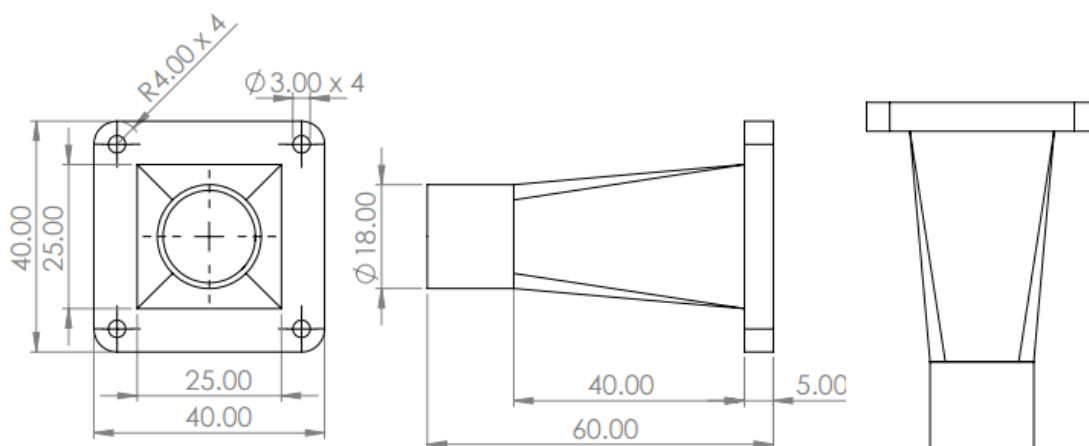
Dimensões do sistema desenhado no CAD, para conectar eletroduto no cooler. Fonte: Autor.
